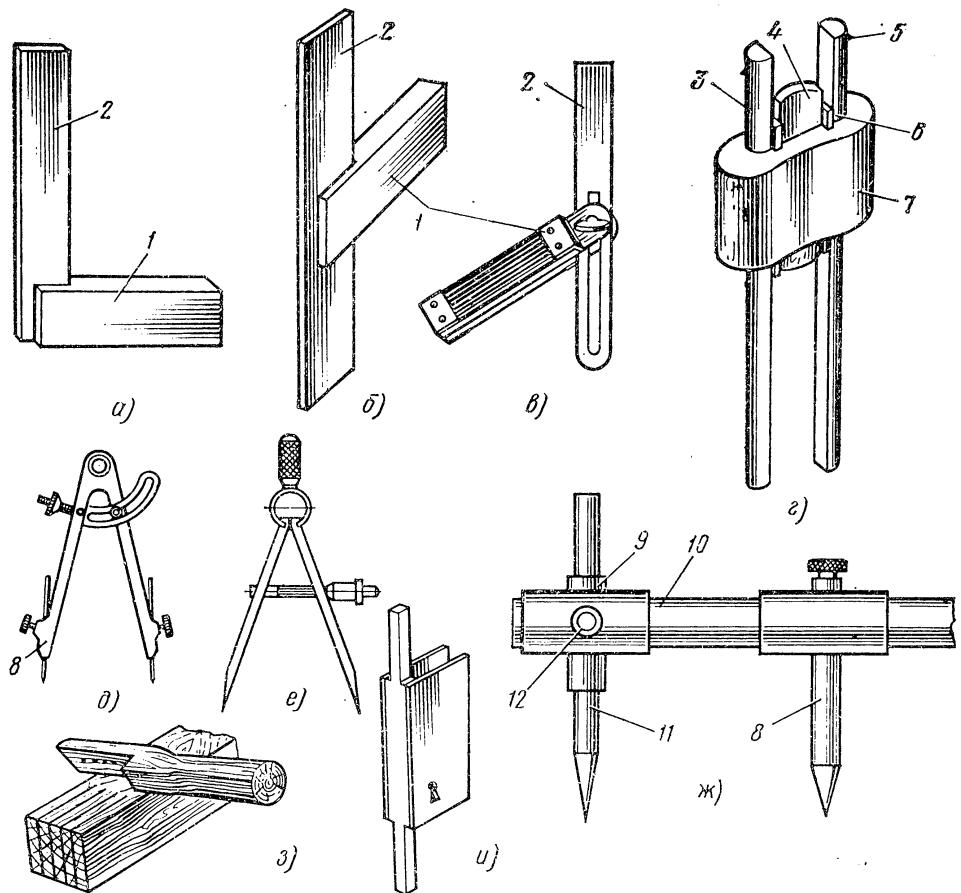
Инструменты и приспособления, применяемые при разметке:
